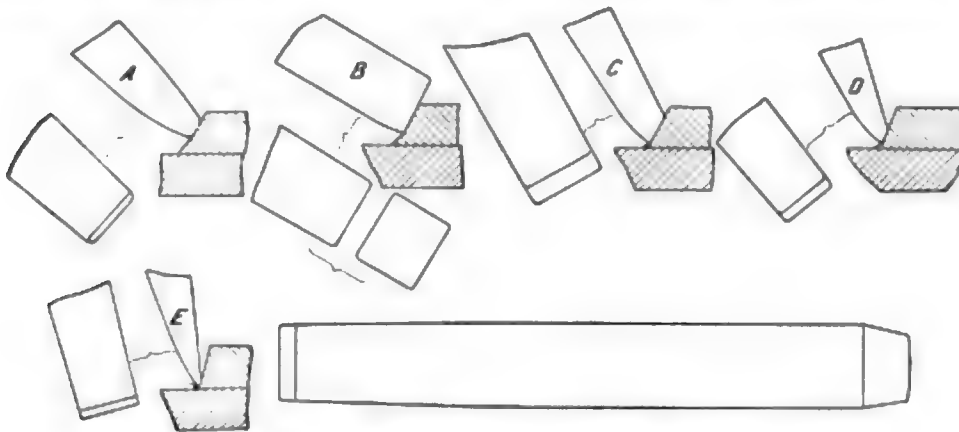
Werkzeuge zum Verstemmen der Blechkanten.
